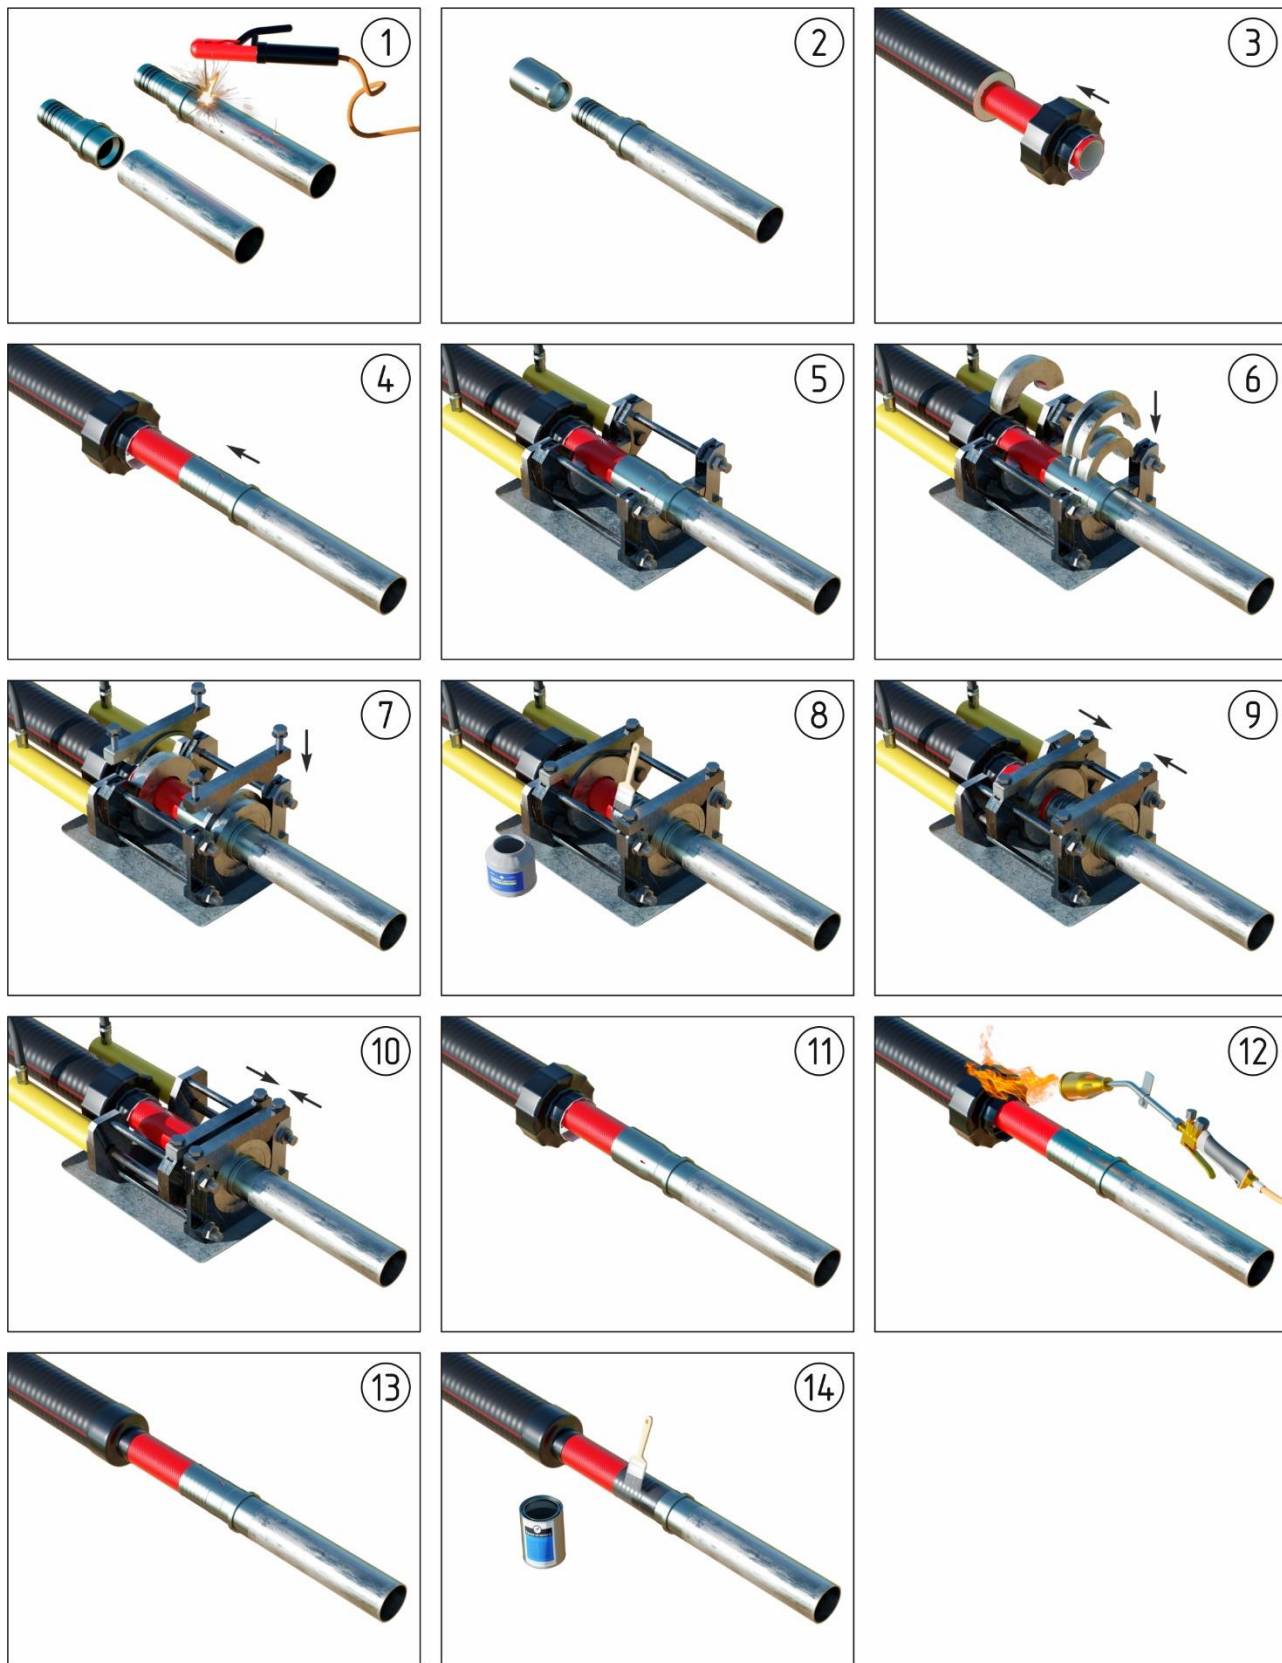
Порядок монтажа фитинга обжимного КОРДФЛЕКС под сварку
